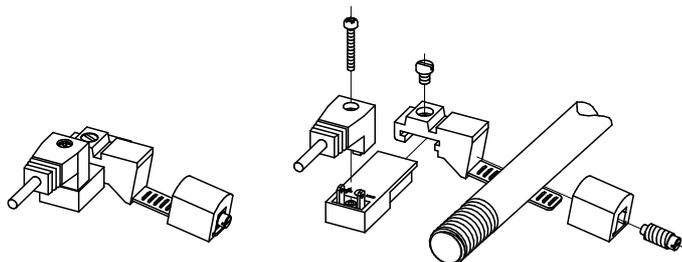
Esempio di montaggio sensore Reed con connettore
